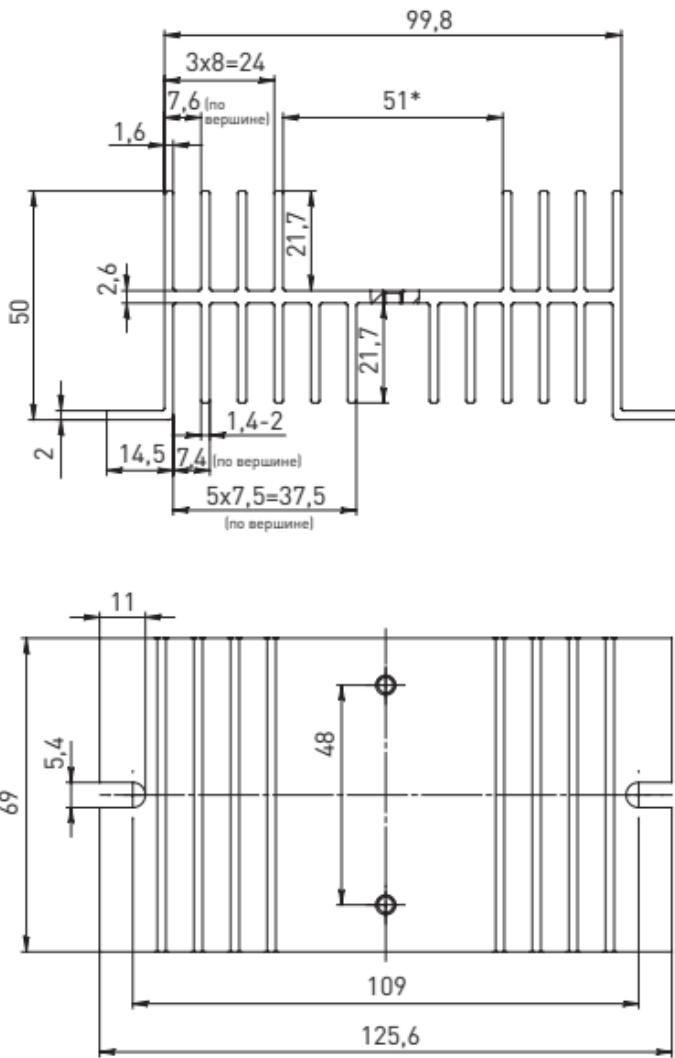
Габаритные размеры радиатора для твердотельного реле 40А
